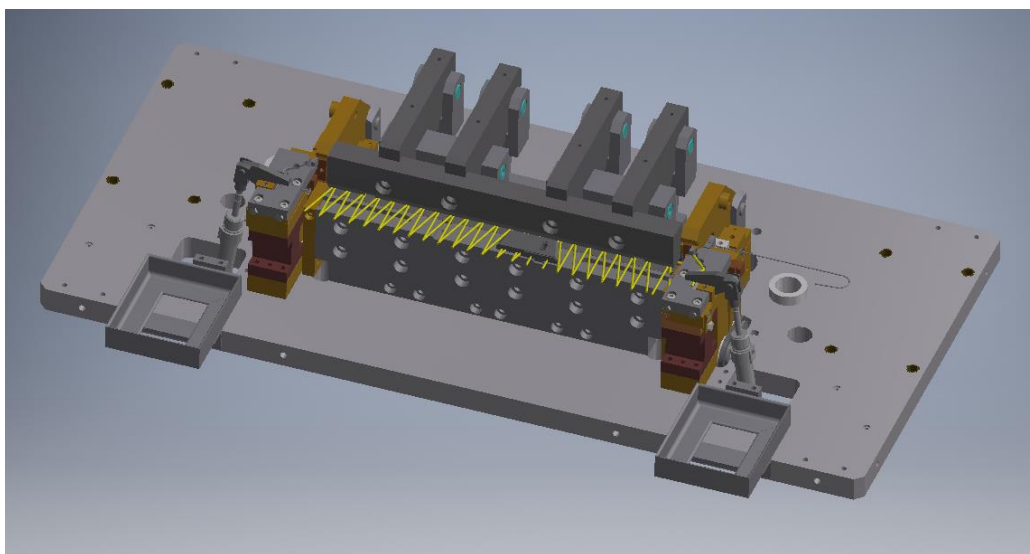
Частина зварювального верстата, в якому використовується пневматичний циліндр
